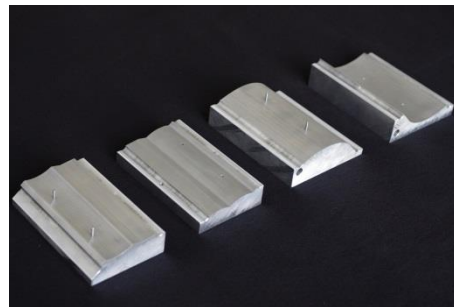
Prägewerkzeuge für Reflektorbleche
